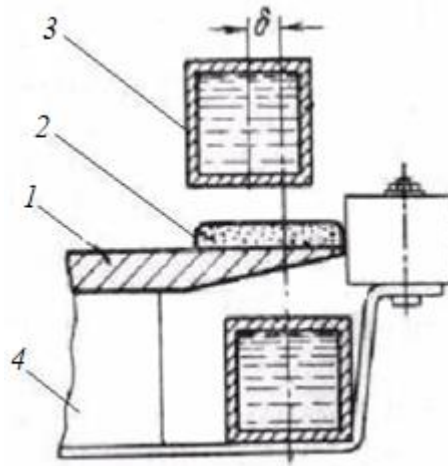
Схема розташування деталі, що наплавляється в індукторі:
